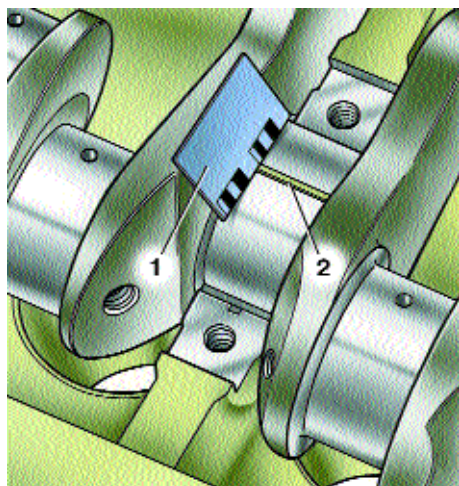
Определение зазора между коренной шейкой и вкладышем по шкале упаковки: 1 – шкала; 2 – калиброванная проволока
